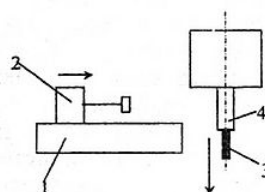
Размещение измерительной головки на многоцелевом станке: 1 - стол; 2 - измерительная головка; 3 - инструмент; 4 - шпиндель станка
